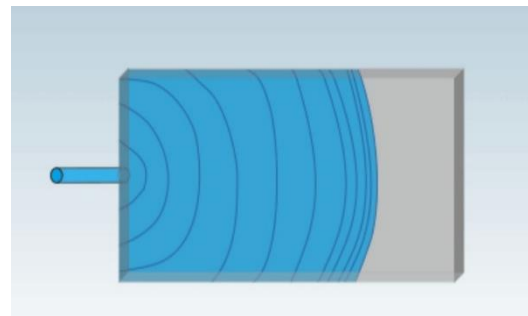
Defecto de tiro corto o “short shot”
